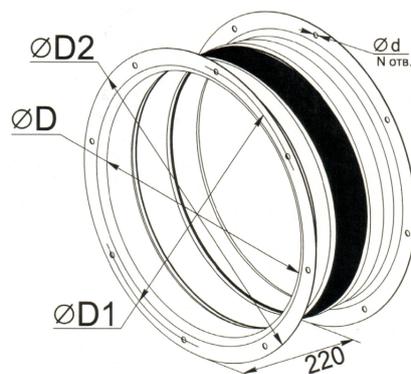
Внешний вид и размеры гибких вставок GVTC
